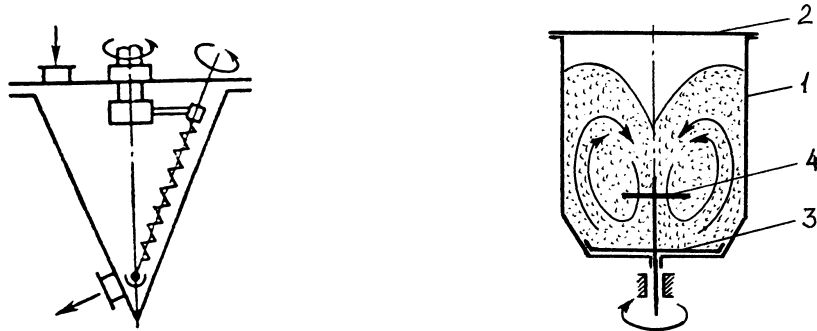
Планетарно-шнековий (а) і відцентровий (б) змішувач (1 – корпус; 2 – кришка; 3 – обертовий диск; 4 – лопать)
